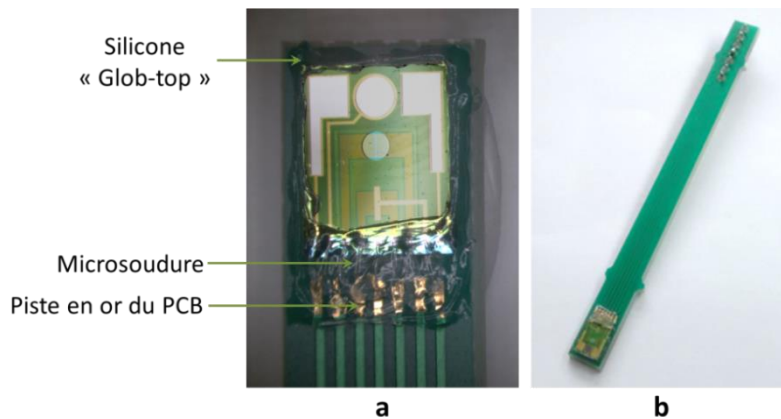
Photos du microcapteur après assemblage sur un PCB
